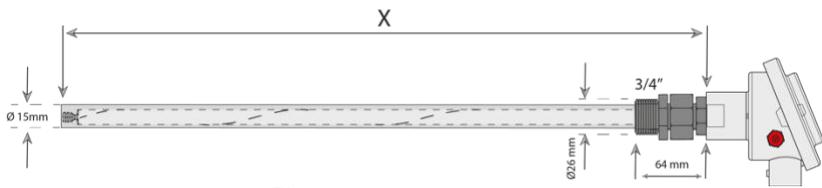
CarboProbe™ HT mit 3/4" Gewinde und Keramikschutzrohr
